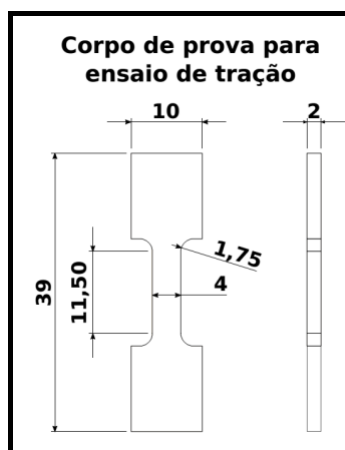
Dimensões dos corpos de prova de tração (dimensões em mm).
